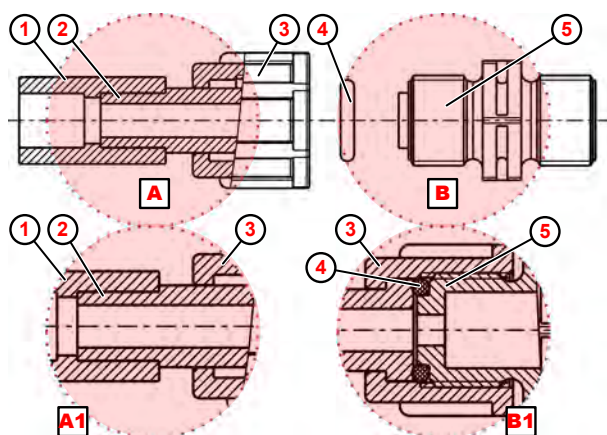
Raccord de conduit avec joint soudé
